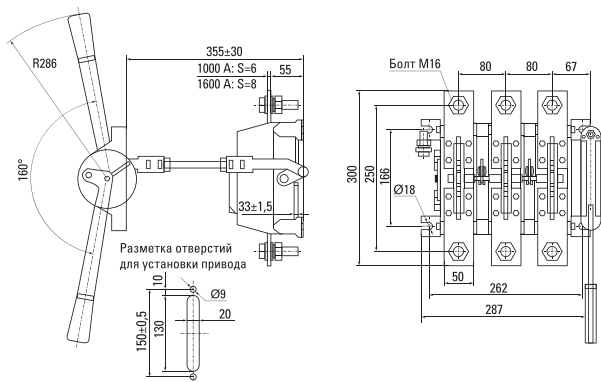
Габаритные и установочные размеры разъединителя типа PE19-41/43 с передней смещенной рукояткой
